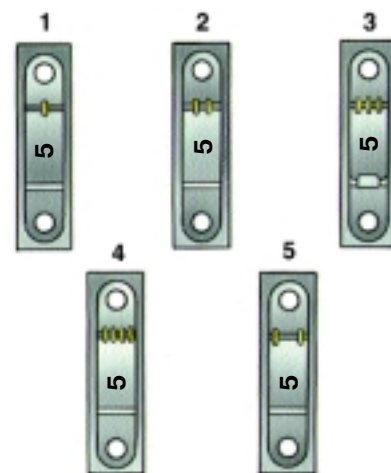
Метки на крышках коренных подшипников (счет опор ведется от передней части двигателя) и условный номер блока цилиндров двигателя мод. 2106–70
